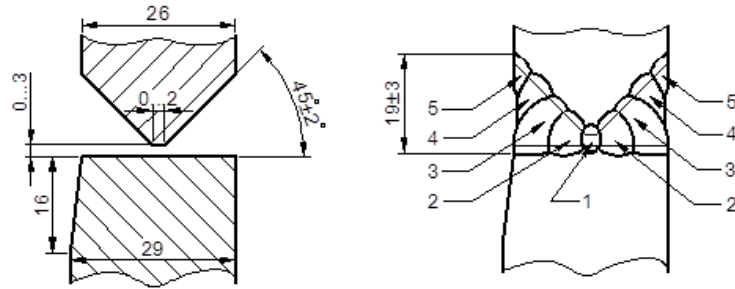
Схема ремонтного узла и последовательность сварки
